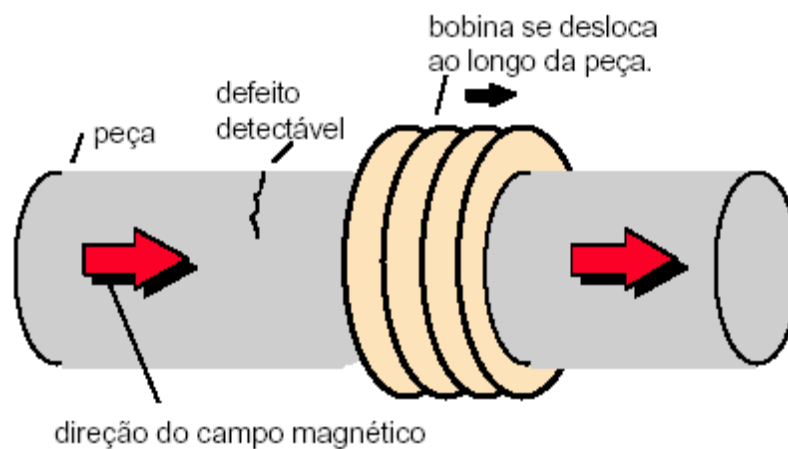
Técnica de Bobina ou Solenóide (ANDREUCCI, 2009).
